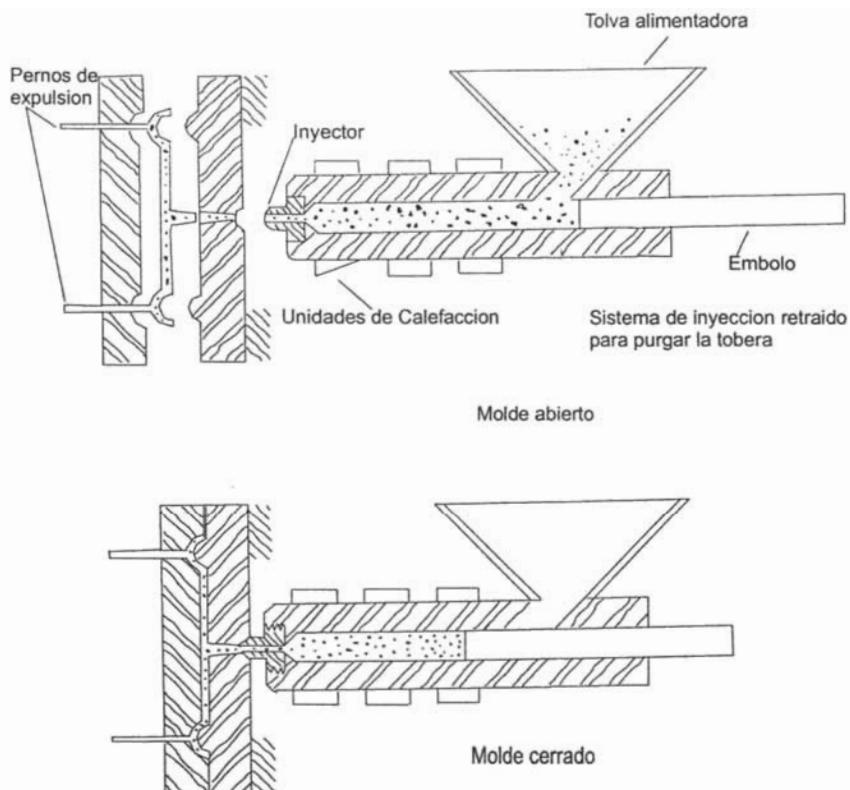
Principio de moldeo por inyección. Un émbolo obliga al termoplástico granulado a moverse hacia delante y pasar a través de una serie de calefactores que lo funden. Luego es inyectado a presión al molde cerrado, donde al plástico fundido se solidifica rápidamente. En seguida se abre el molde y se saca la pieza junto con el bebedero del molde. Este ciclo se repite automáticamente.⁸
